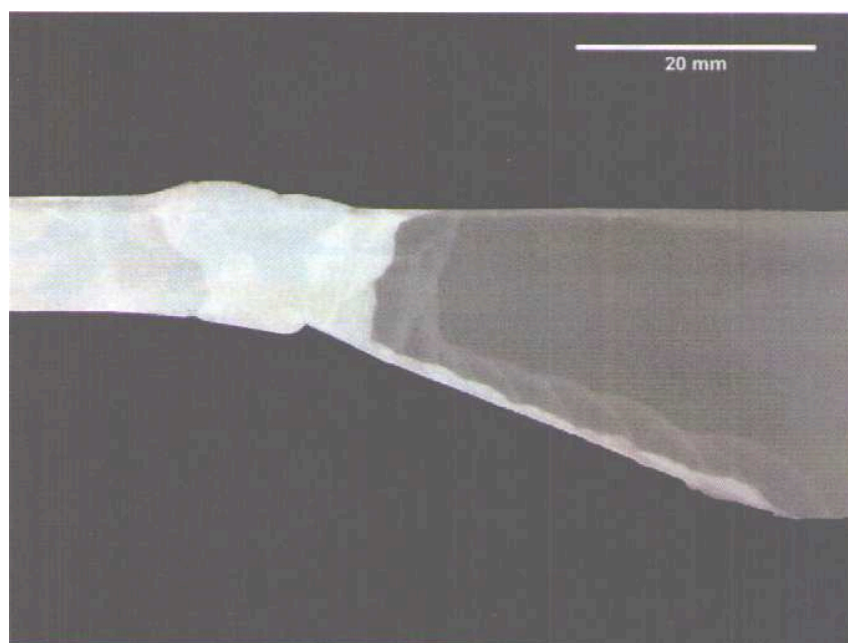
Aspecto macrográfico da junta soldada (fonte: autor)
